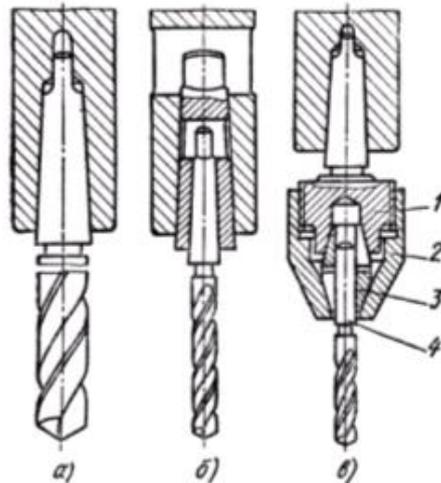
Закрепление инструмента на сверлильных станках: а – шпиндель; б – коническая втулка; в – цанговый патрон; 1 – корпус патрона; 2 – втулка; 3 – цанга; 4 – хвостовик инструмента.
